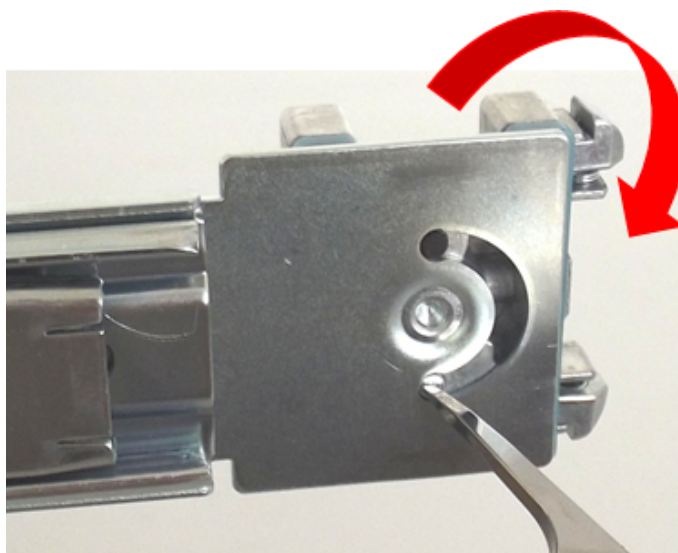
Drücken des Bolzens auf der Innenseite der Halterung
